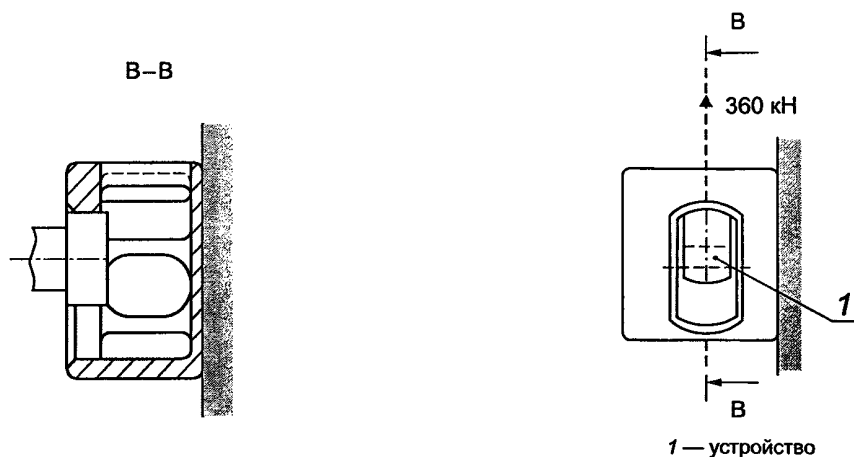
Испытание крепления для железнодорожной перевозки
